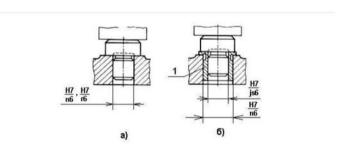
Варианты установки точечных опор в корпусе приспособления: a) непосредственно; б) через переходную втулку
